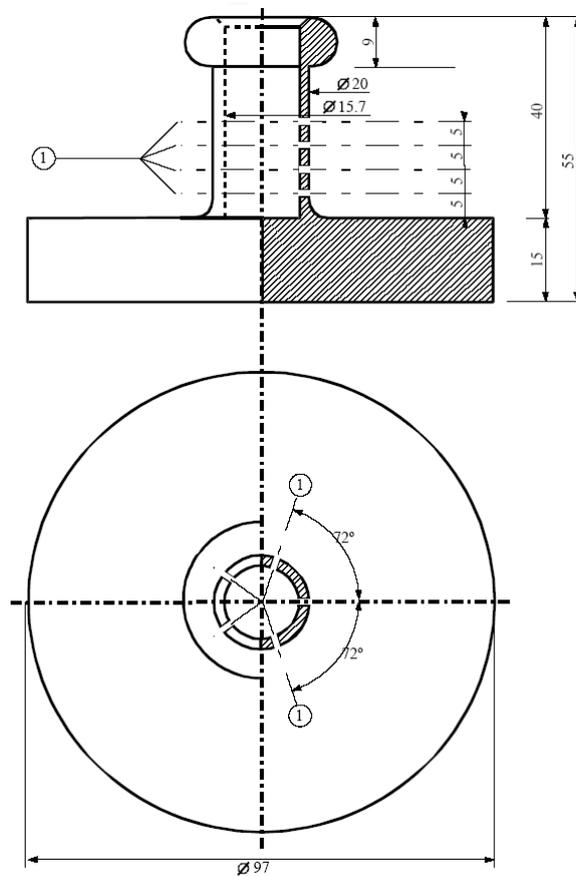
Cilindro cavo di bronzo, chiuso da un lato; vista in pianta e sezione verticale
